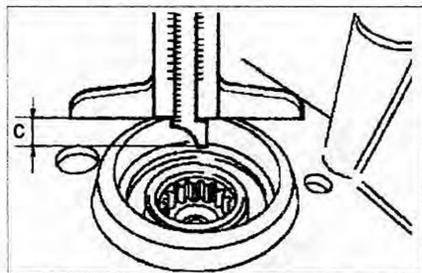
Измерение расстояния С от верхней кромки седла подшипника до отверстия под подшипник в корпусе коробки передач, используя штангенциркуль.
